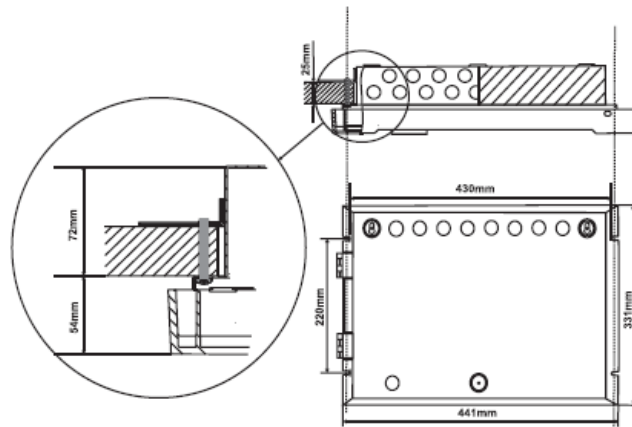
Öffnungen für Einbaumontage. Ansicht mit fixierten Montagewinkeln an der Wand und Schrauben, die das Gehäuse festhalten.
